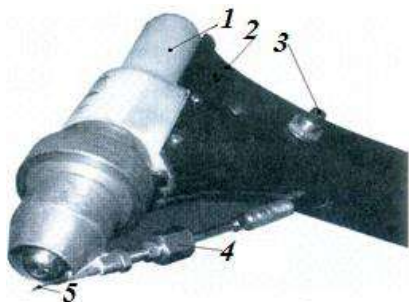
Плазматрон для полуавтоматической сварки металлов
